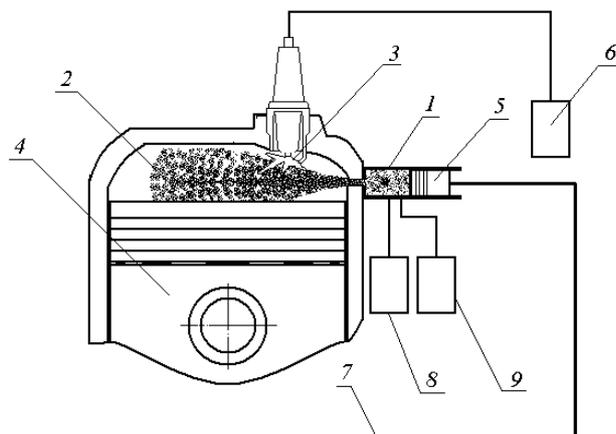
Схема конструкции для реализации унифицированного рабочего процесса: 1 – компрессор-форсунка; 2 – факел обогащенной ТВС; 3 – искровой разряд; 4 – поршень; 5 – поршень компрессор-форсунки; 6 – коммутатор системы зажигания; 7 – привод компрессор-форсунки от вала двигателя (условно); 8, 9 – устройства дозирования топлива и воздуха для компрессор-форсунки
